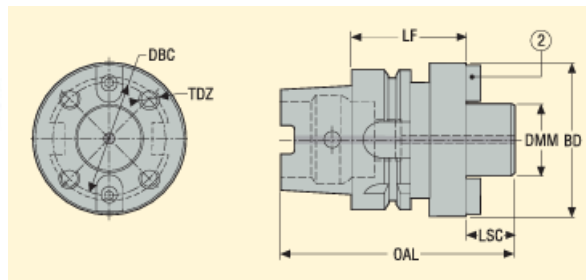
Державка HSKA100-SMF60-075 [16, с.76]
